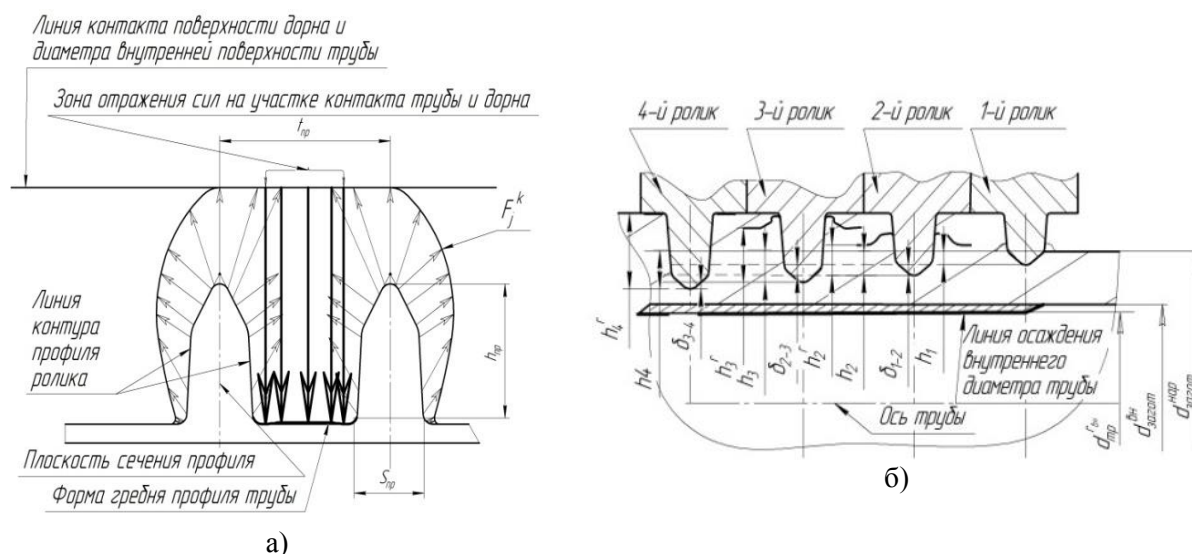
Воздействие сил на реальный профиль и формирование границ поверхностей гребней и боковых поверхностей профиля.
